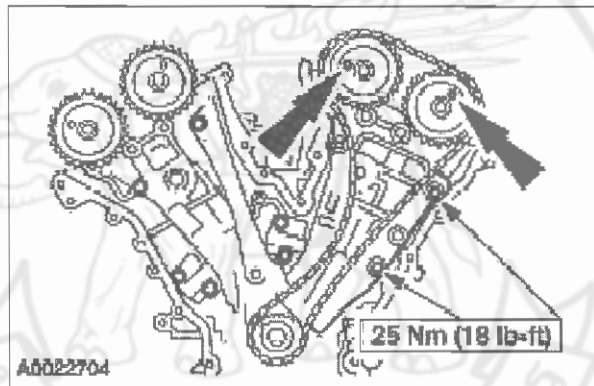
การติดตั้ง Crankshaft sprocket
